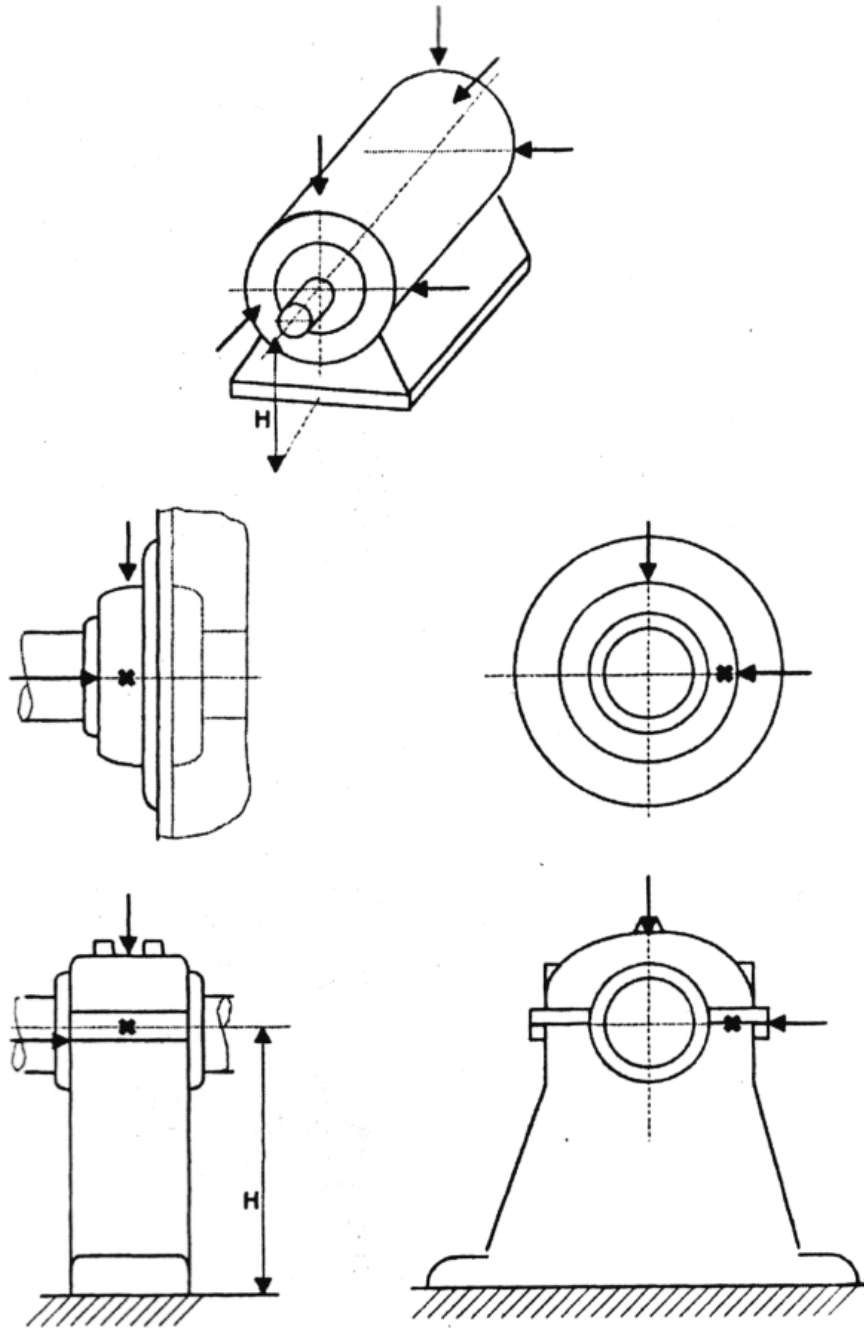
Места установки датчиков на корпусе электрической машины и подшипниковых опорах
